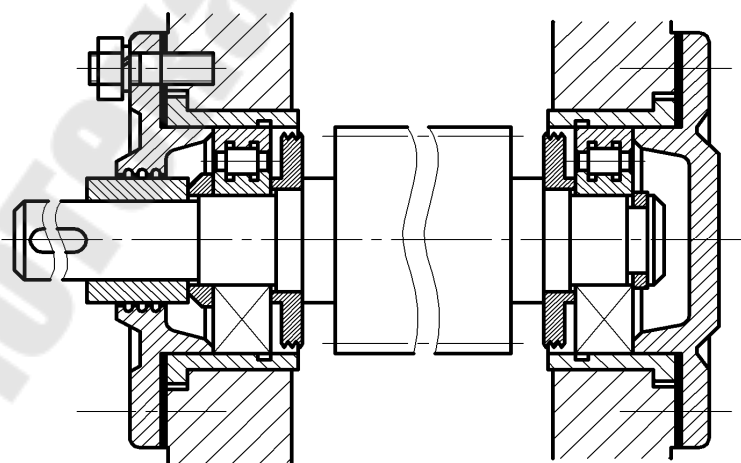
Вал на радиальных роликовых подшипниках; с «плавающим» правым подшипником (подшипник без бортов на наружном кольце)
